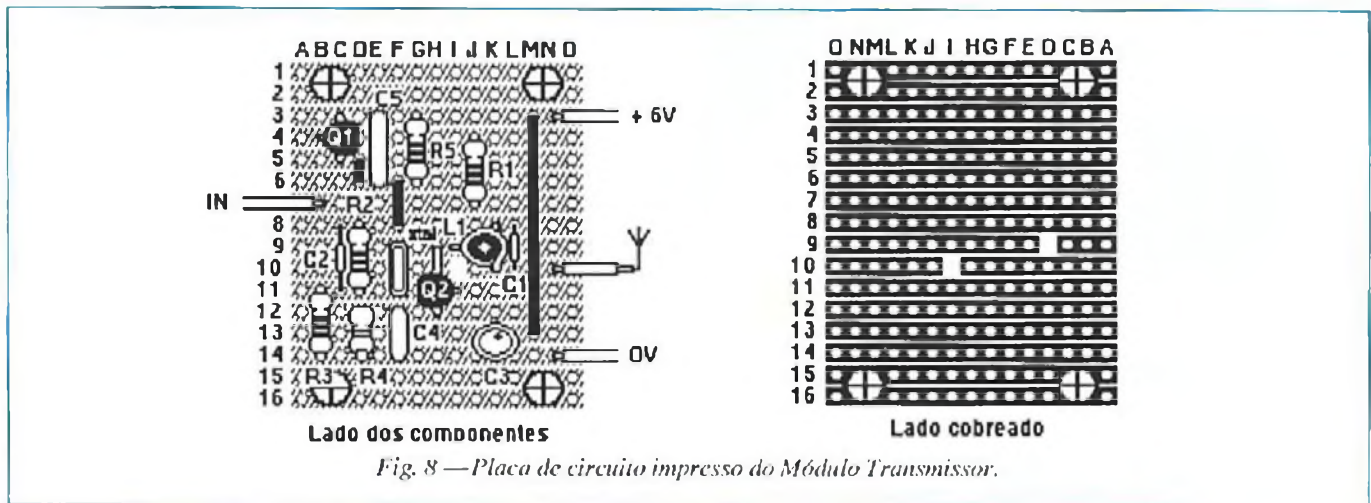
Placa de circuito impresso do Módulo Transmissor.
